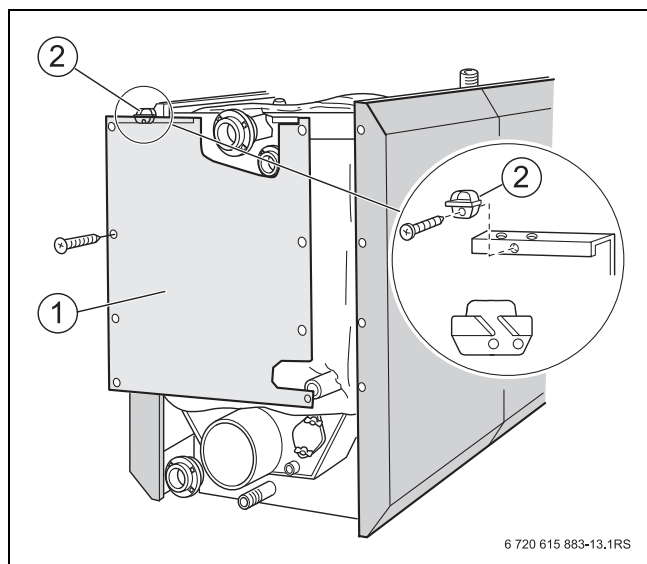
Aparafusar painel traseiro (tamanho da caldeira 400...640 kW)
